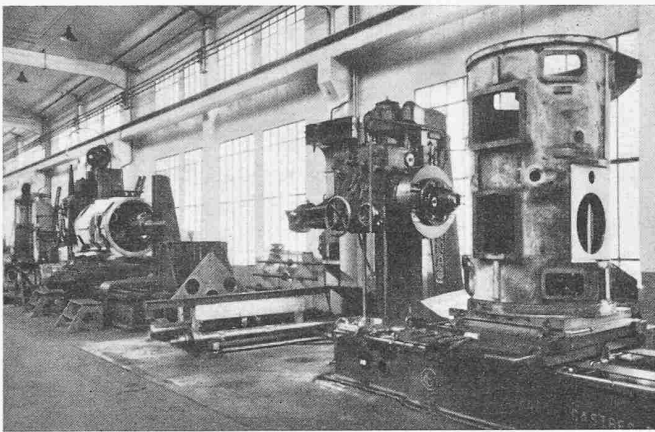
Usinage du carter d'un générateur de 1000 CV
